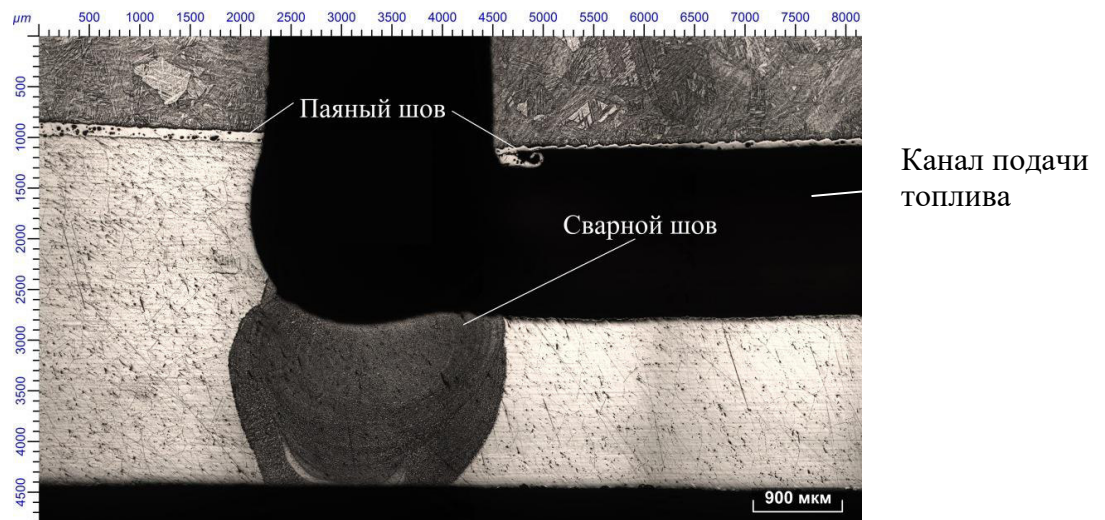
Сварной шов паяных оболочек из стали 12X18H10T-ВД
